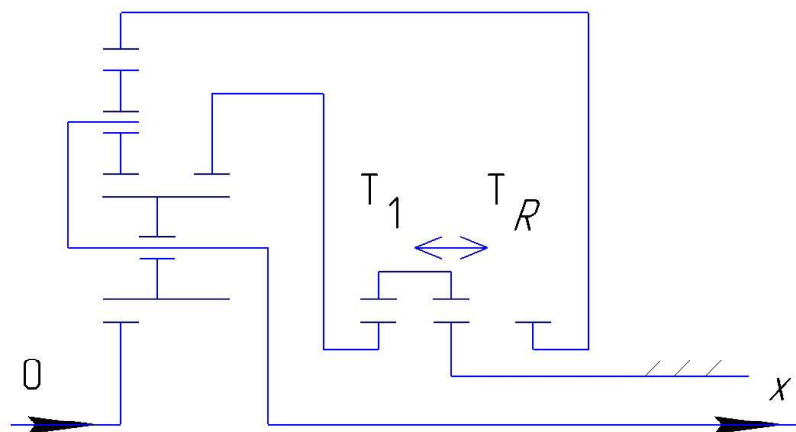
Упрощенная кинематическая схема бортового реверс-редуктора: тормоза T_1 и T_R
